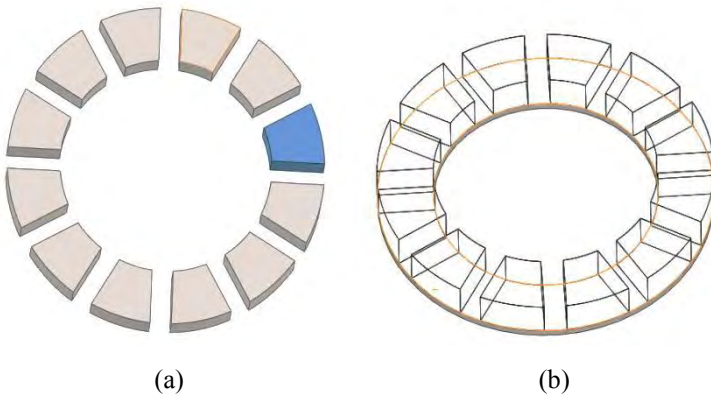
Sketsa stator motor *axial flux* BLDC
